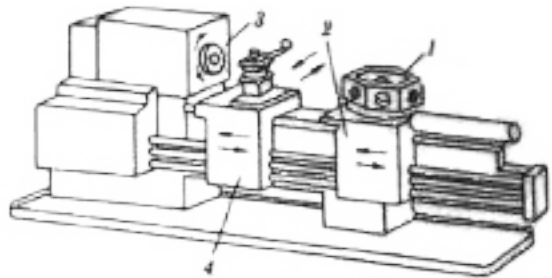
Токарно-револьверний верстат з горизонтальним розташуванням револьверної головки
